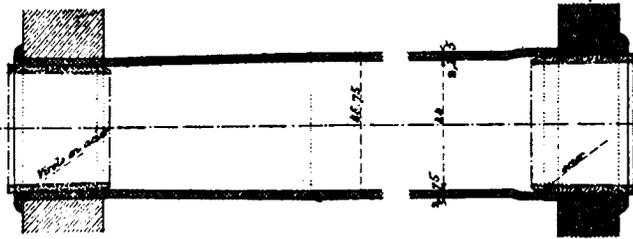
Montage des tubes de chaudières des Chemins de fer de l'Est.
